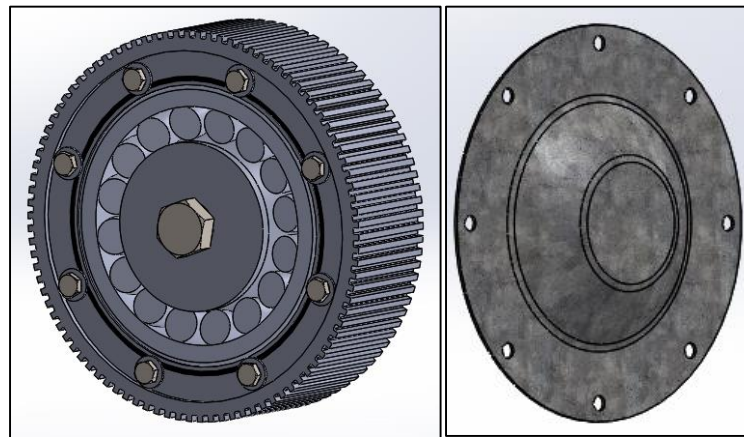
Imagen izq.: Vista de un rodillo sin tapa de protección. Aquí se observa el oring de sellado y la sujeción del rodamiento con el tornillo y la arandela de vuelo ancho. Imagen der.: Tapa de rodamiento.
